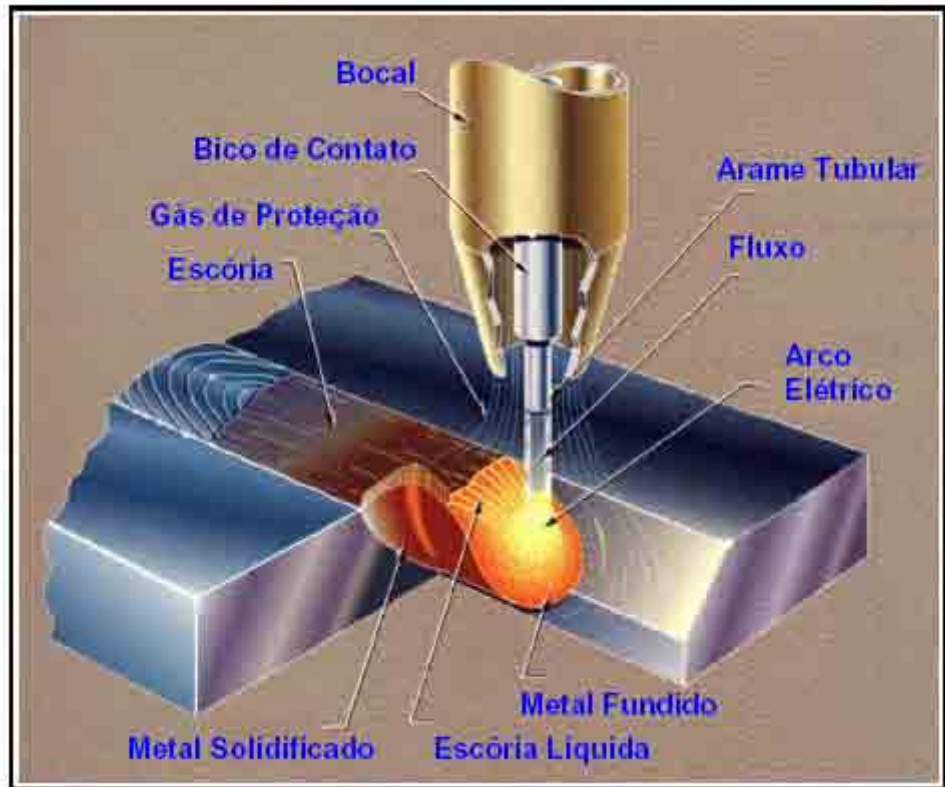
Esquema ilustrativo da soldagem com arame tubular com proteção adicional de gás (Fonte: Welding Handbook (1991)).
